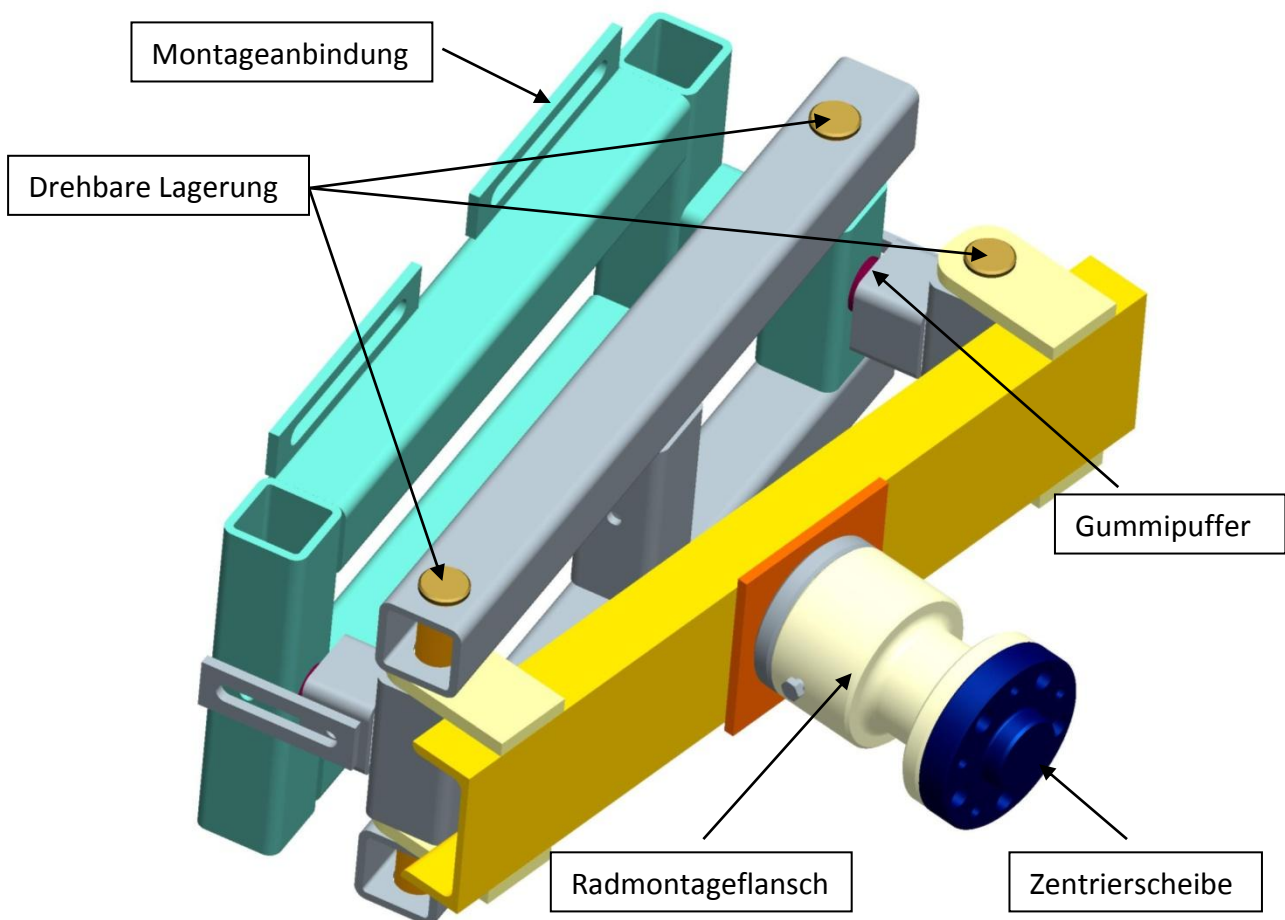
Detailansicht des Impact-Test Prüfstandes.
